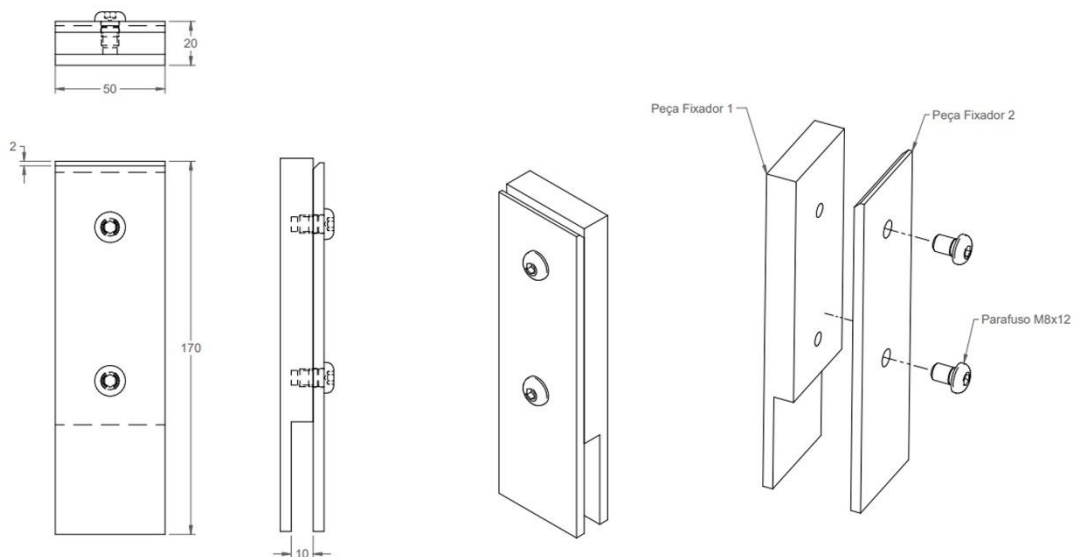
Medidas da pinça de fixação em construção soldada
